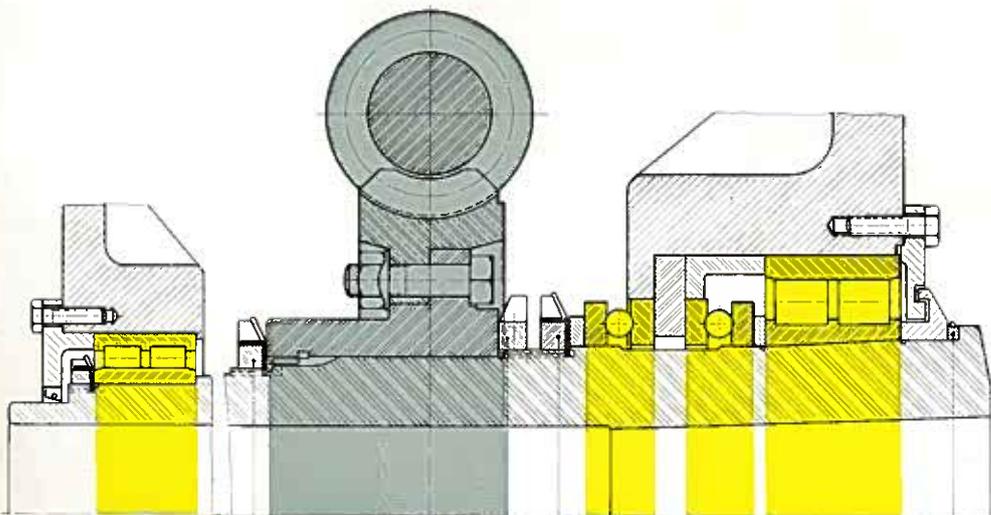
Einbaubeispiel für CAVEX-Schneckenrad (Frässpindeltrieb)
